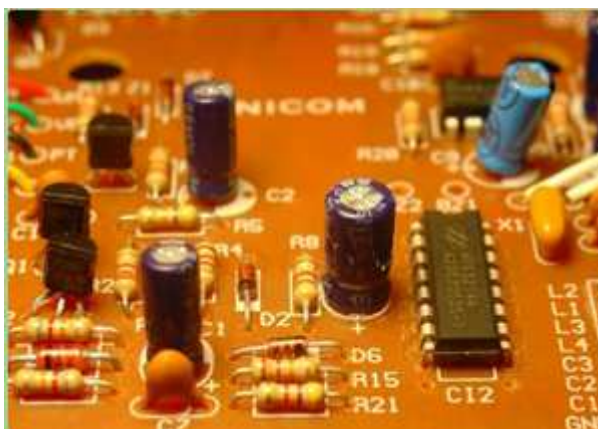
Placa de componentes *“through hole”*. Fuente: [10].
